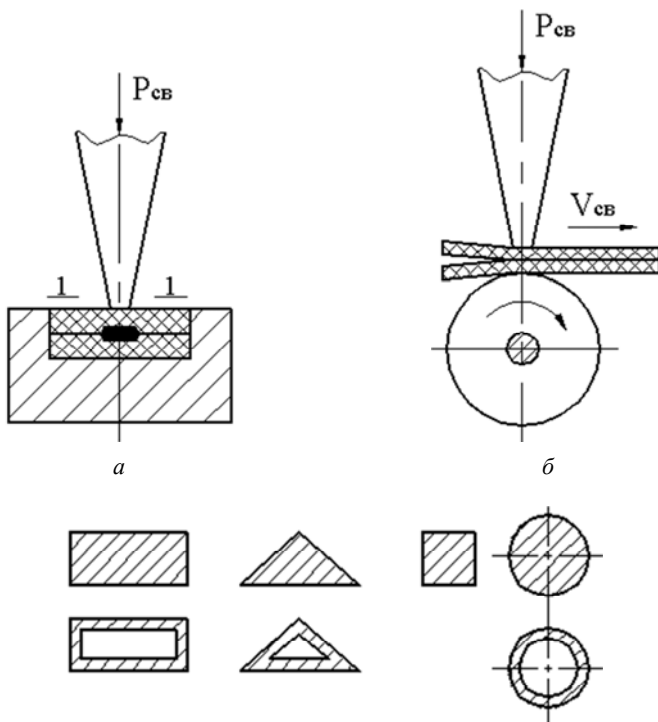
Схемы контактной ультразвуковой сварки:
